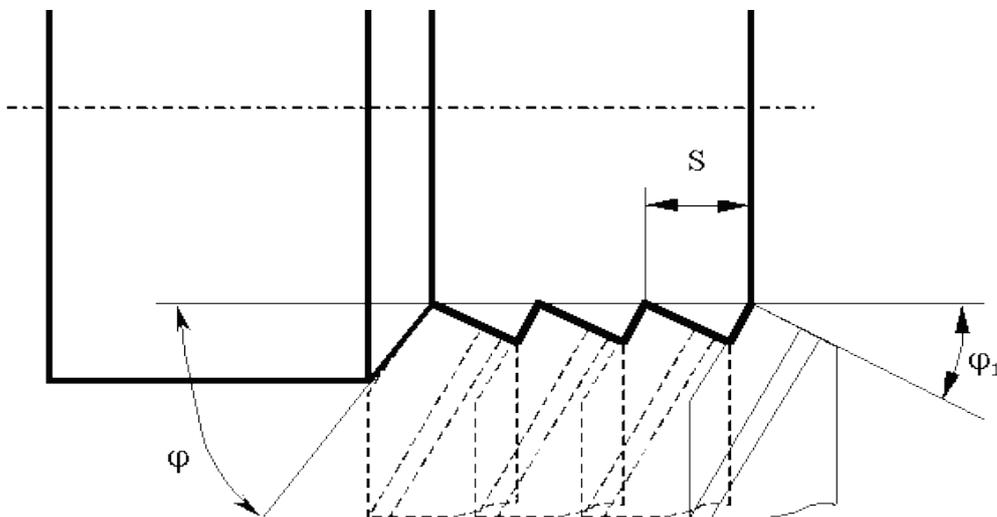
Образование шероховатости на поверхности детали от движения режущих кромок резца
